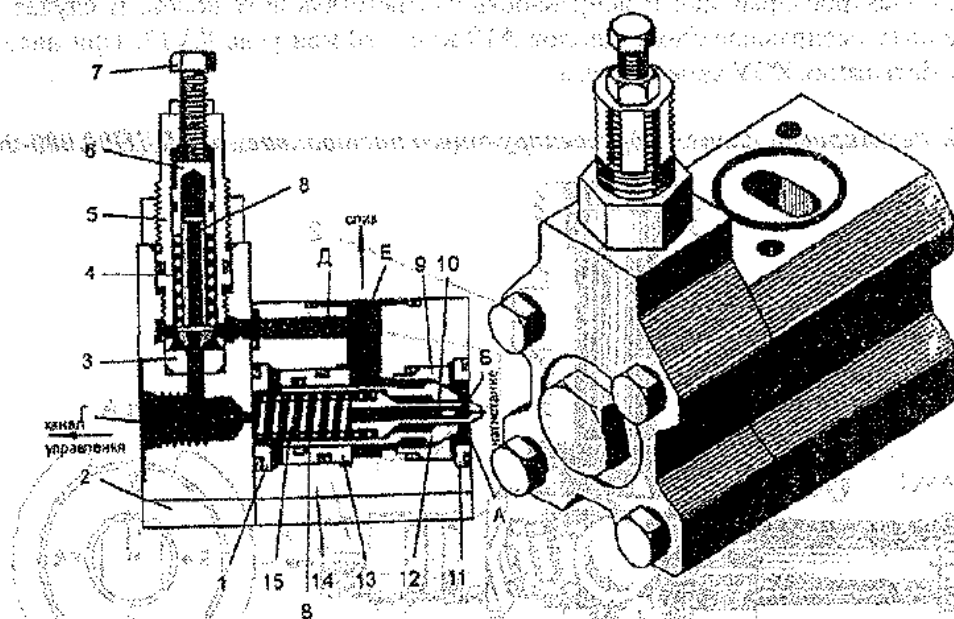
Клапан напорный КН 50.12,5 или 108.00.000В: 1, 11-шайбы; 2-крышка; 3, 9-седла; 4, 15-пружины; 5, 13-втулки; 6-поршень; 7-болт; 8-запорный элемент; 10-клапан; 12-клапан; 14-корпус; А-полость нагнетания; Б-дроссельное отверстие; В-полость внутренняя; Г-полость выхода потока; Д-полость сливная предохранительного клапана; Е-полость слива
